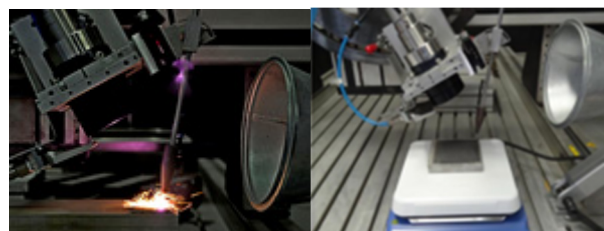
Beispiele Laserauftragschweißen [6]
